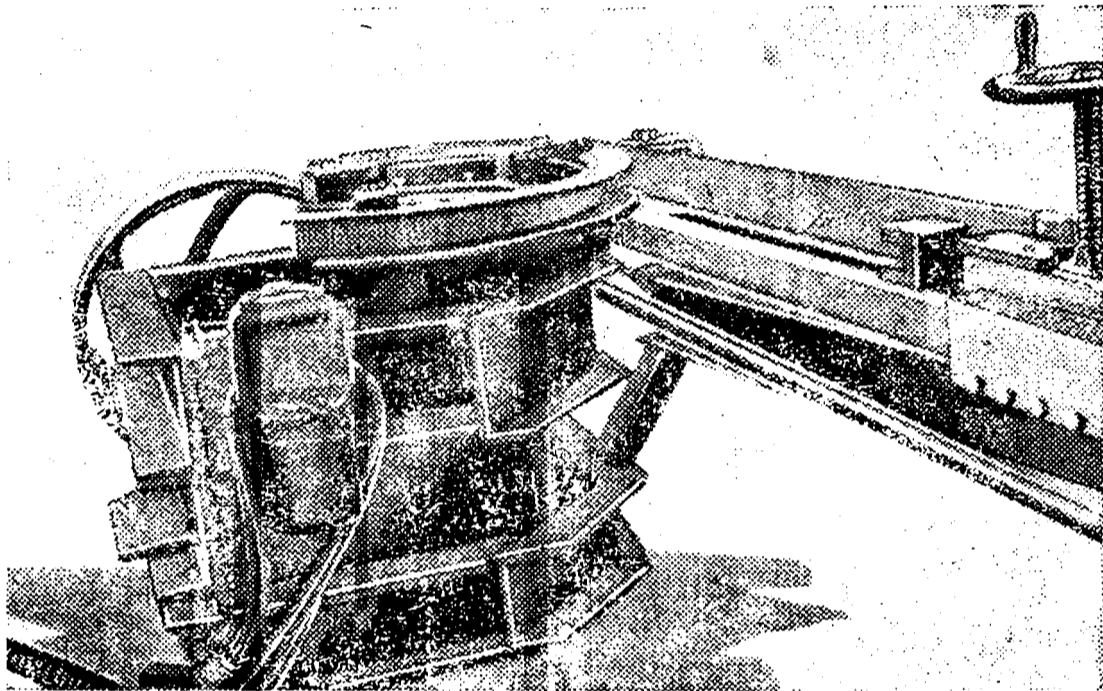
Станок для гнутья хвойных полубобдьеv и косяков
